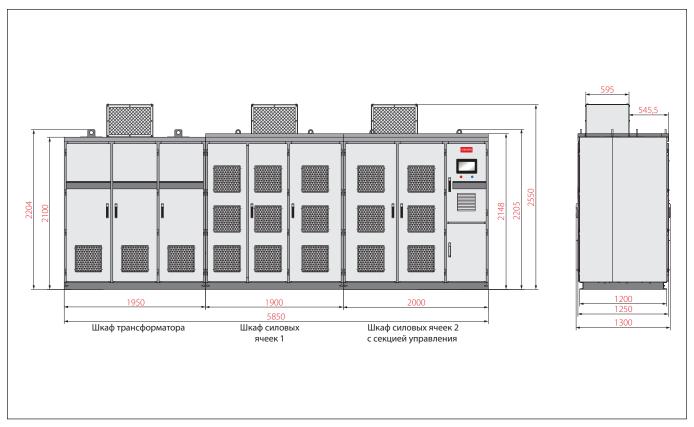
Корпус RC02 на напряжение 10 кВ
